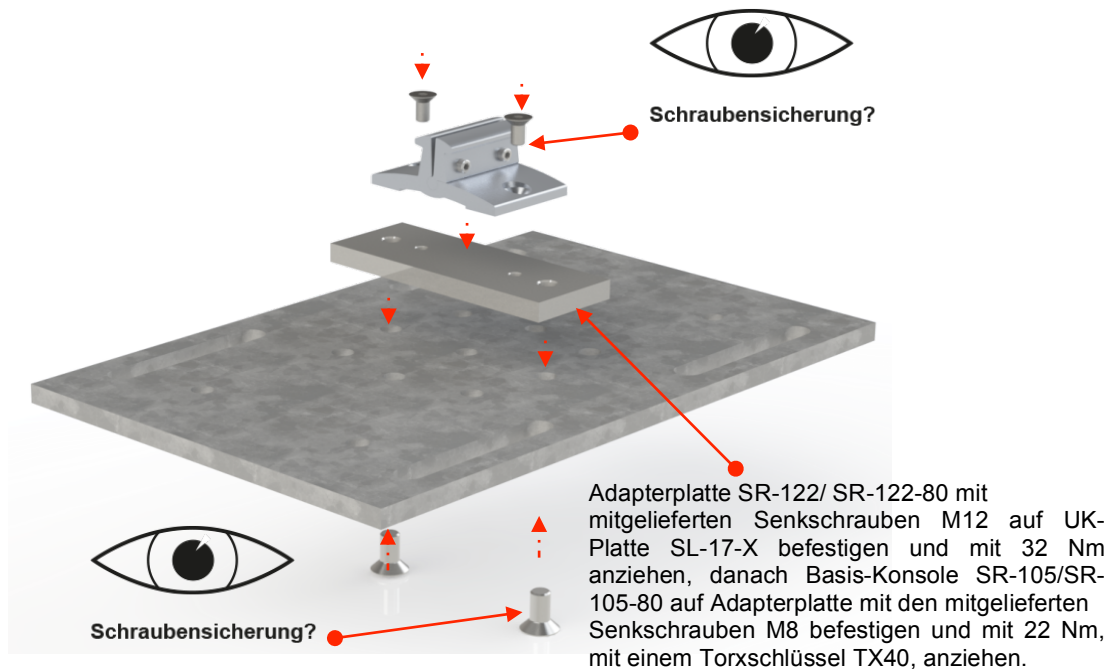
Montage Basiskonsole SR-105 auf Adapterplatte SR-122 für UK-Platten SR-017
